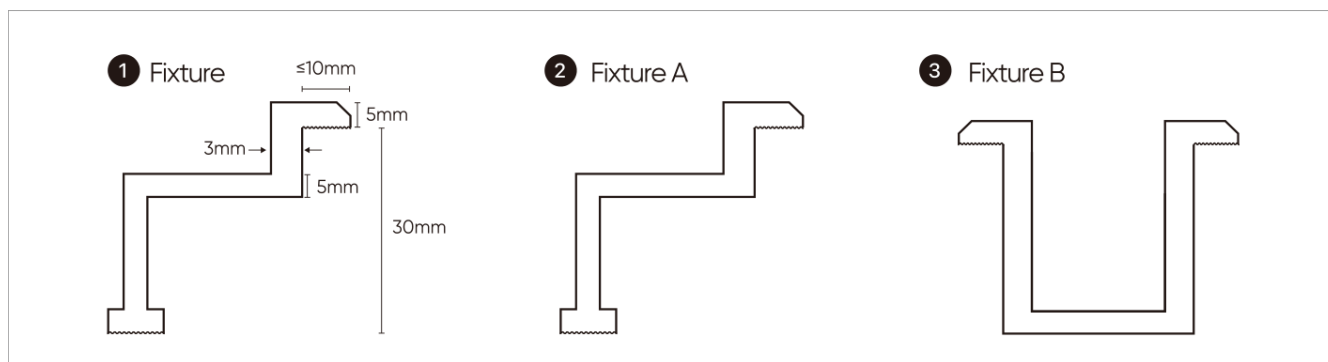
Schéma svorky pro běžný FV modul. Fixture = svorka
